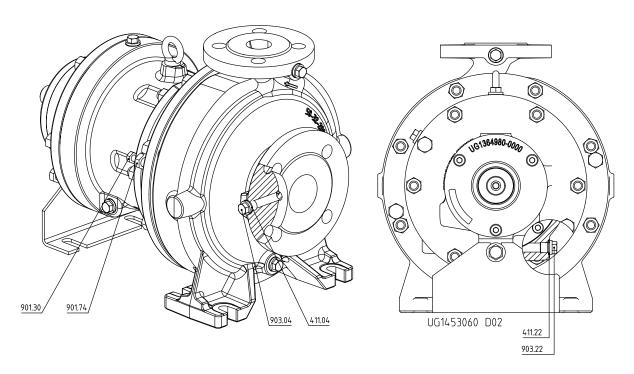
Крепление крышки с напорной стороны на корпусе насоса для исполнения с привинчиваемой крышкой корпуса
